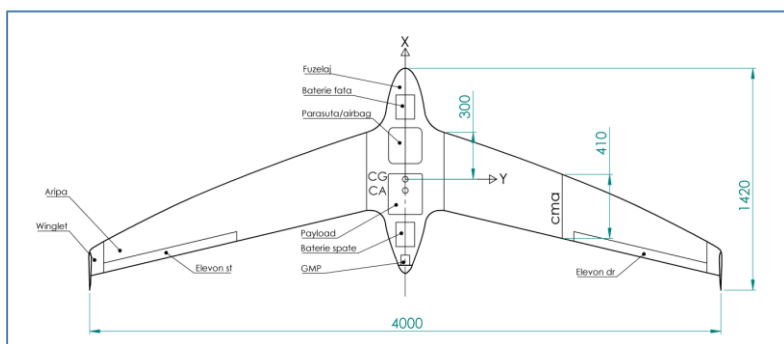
Vedere în plan (deasupra) UAV-BWB
